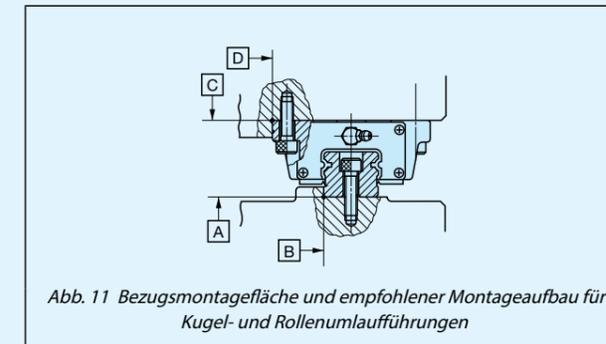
Bezugsmontagefläche und empfohlener Montageaufbau für Kugel- und Rollenumlauführungen
